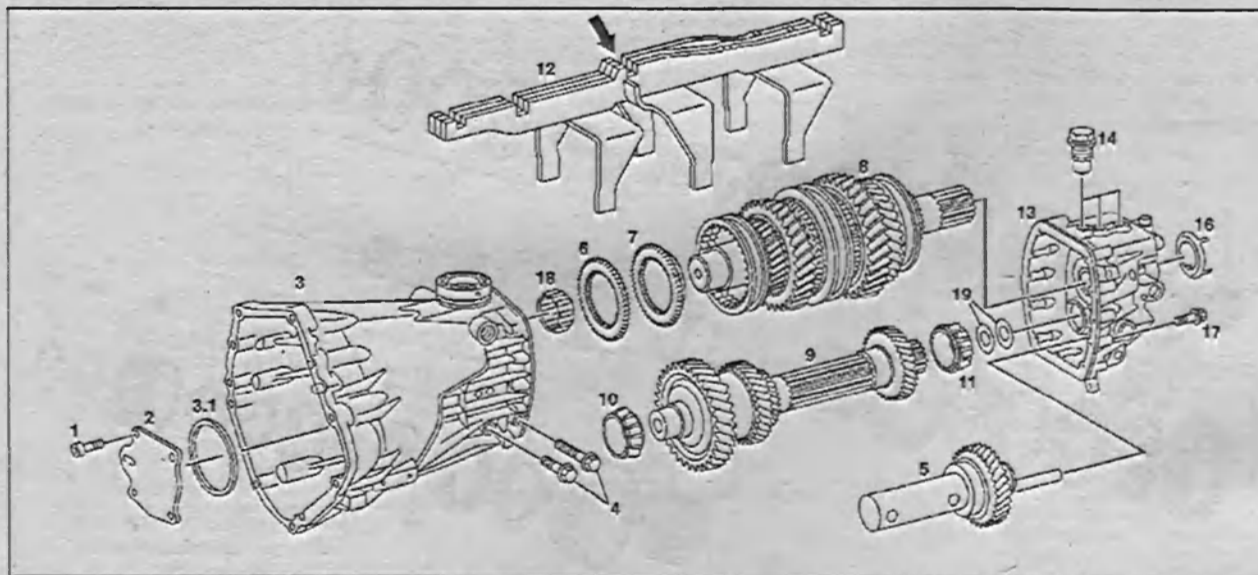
б. Вторичный и промежуточный валы коробки передач 711.612/613:
